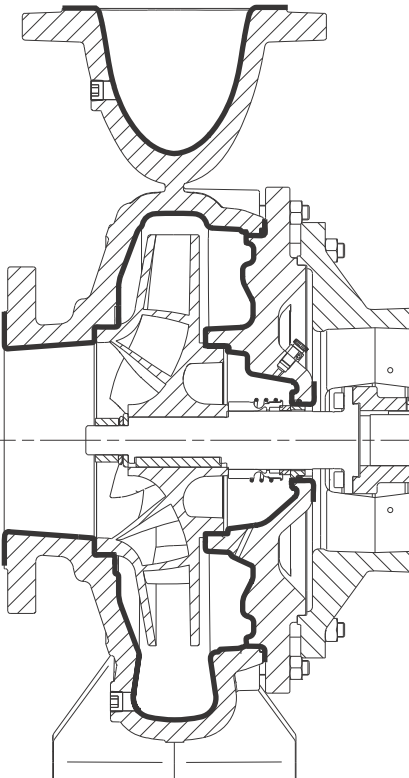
Schnittzeichnung von Pumpen mit Beschichtung für Seewasser bis 25 °C
